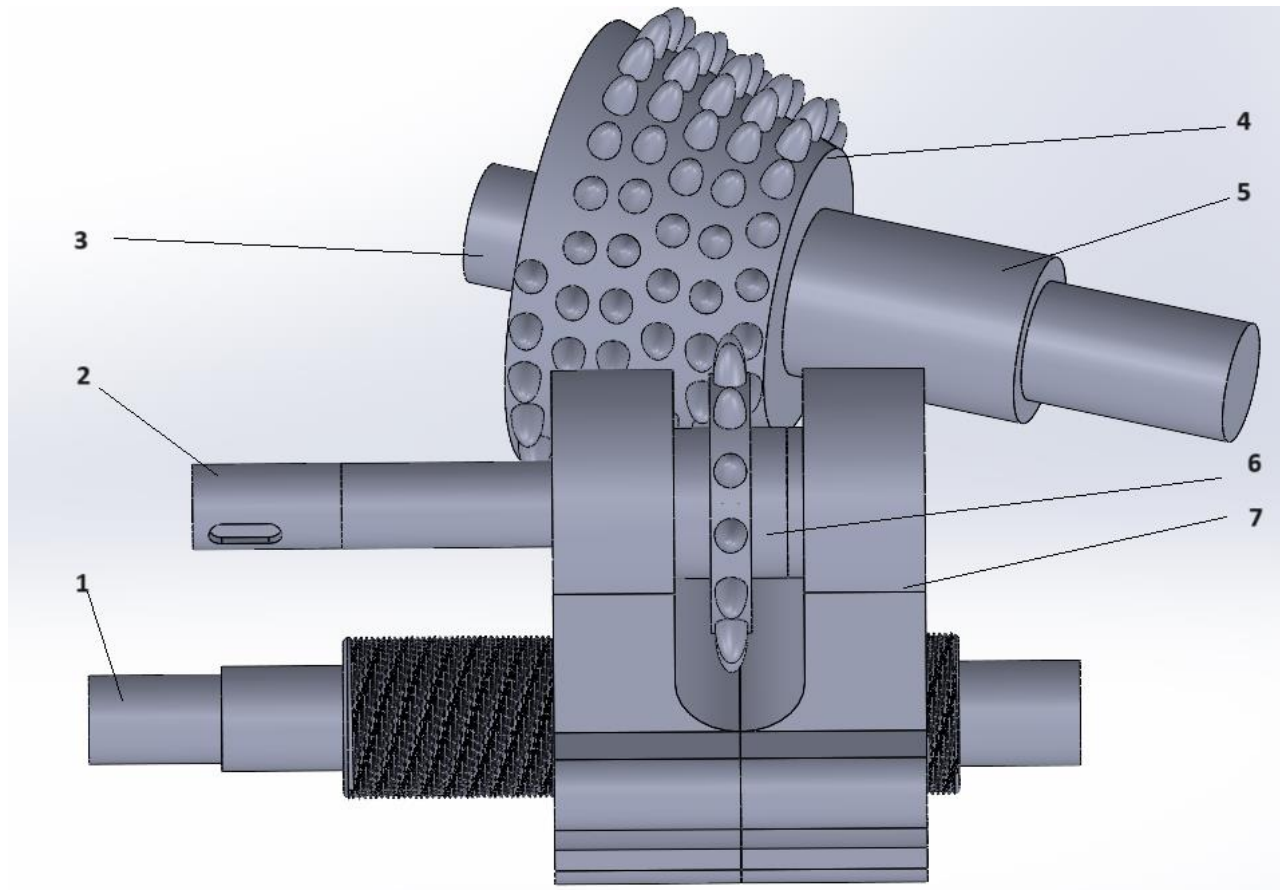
Схема компоновки редуктора, вид сбоку
